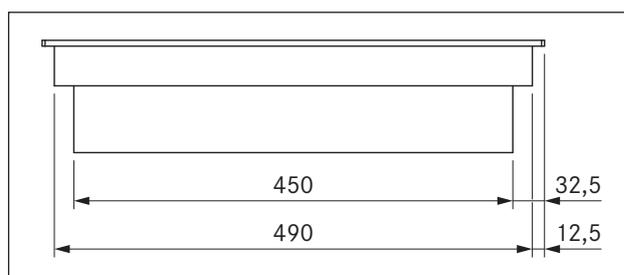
Dimensões do aparelho CKIW, vista lateral
